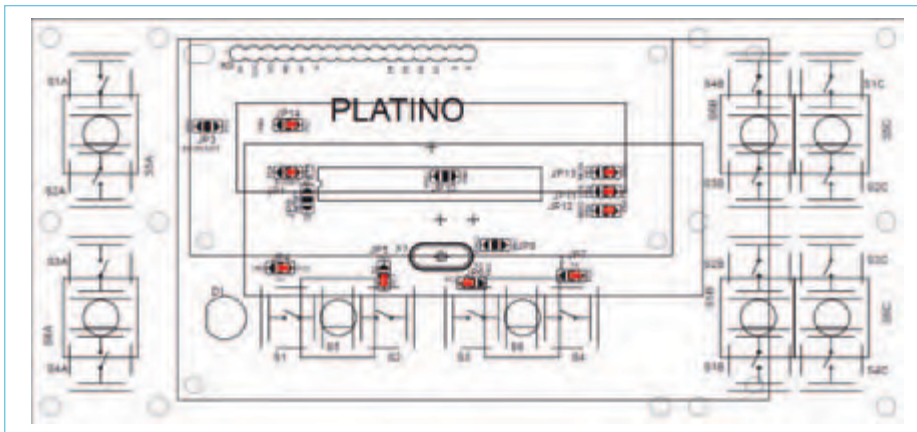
¡En la parte superior ("TOP") los puentes de soldadura!
